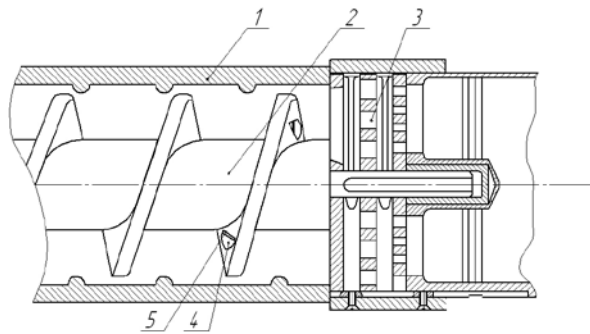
Робочий шнек попереднього подрібнення : 1 - корпус; 2 - шнек; 3 - різальний механізм; 4 - отвори; 5 - плоскі ножі
